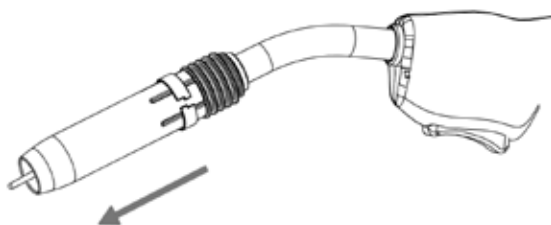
Порядок заправки сварочной проволоки.
